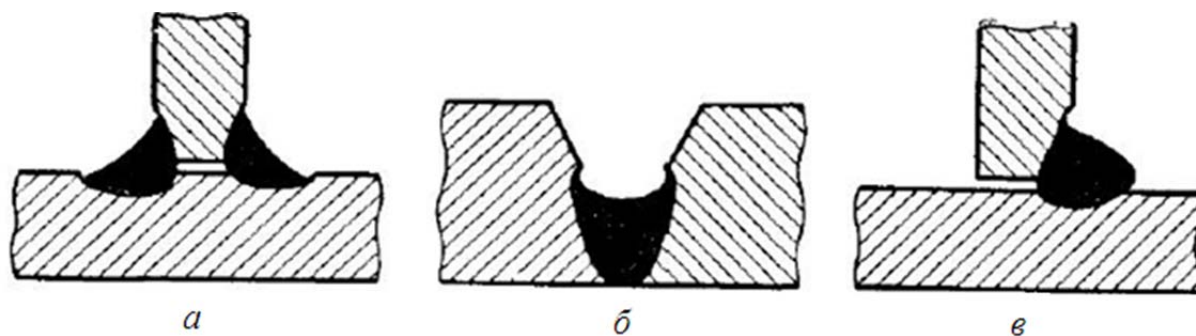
Підрізи: *а* — двосторонній при зварюванні кутового шва; *б* — двосторонній при зварюванні першого шару багатшарового стикового шва; *в* — однобічний з напливом на другу кромку при зварюванні кутового шва
